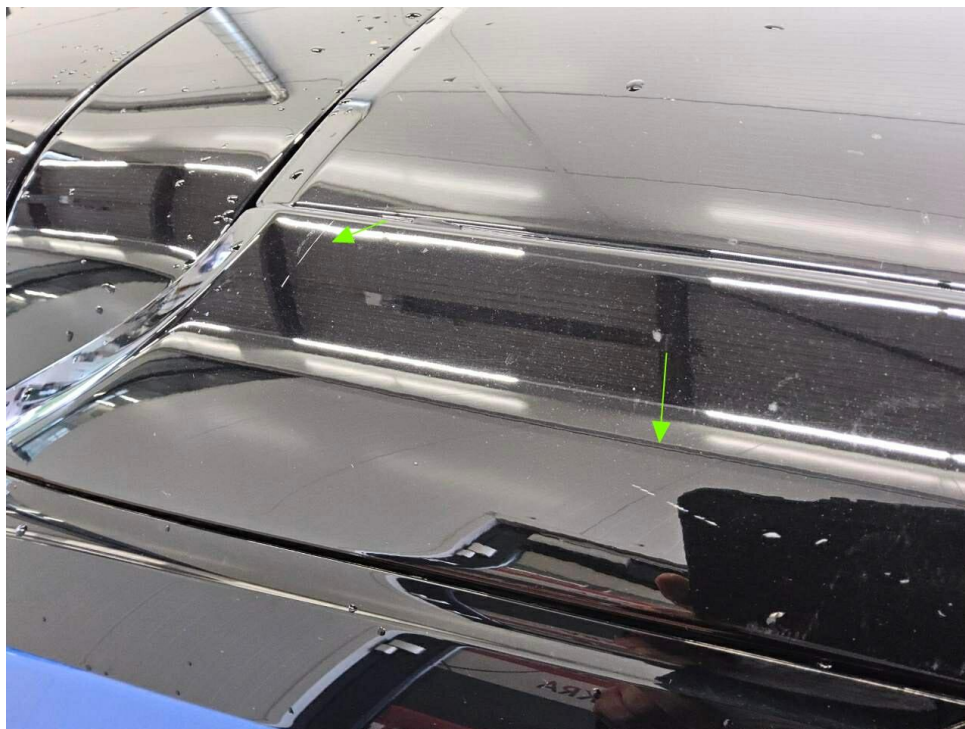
Dachrahmen rechts Lackierung, zerkratzt, lackieren mit Lackaufbau
